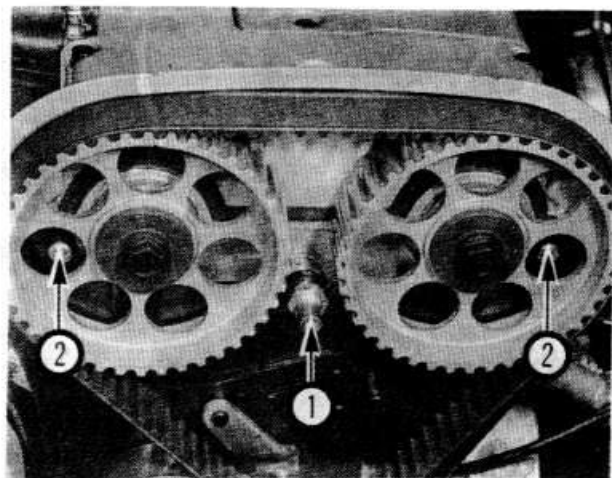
Верхняя шпилька (1) и верхние болты (2)
